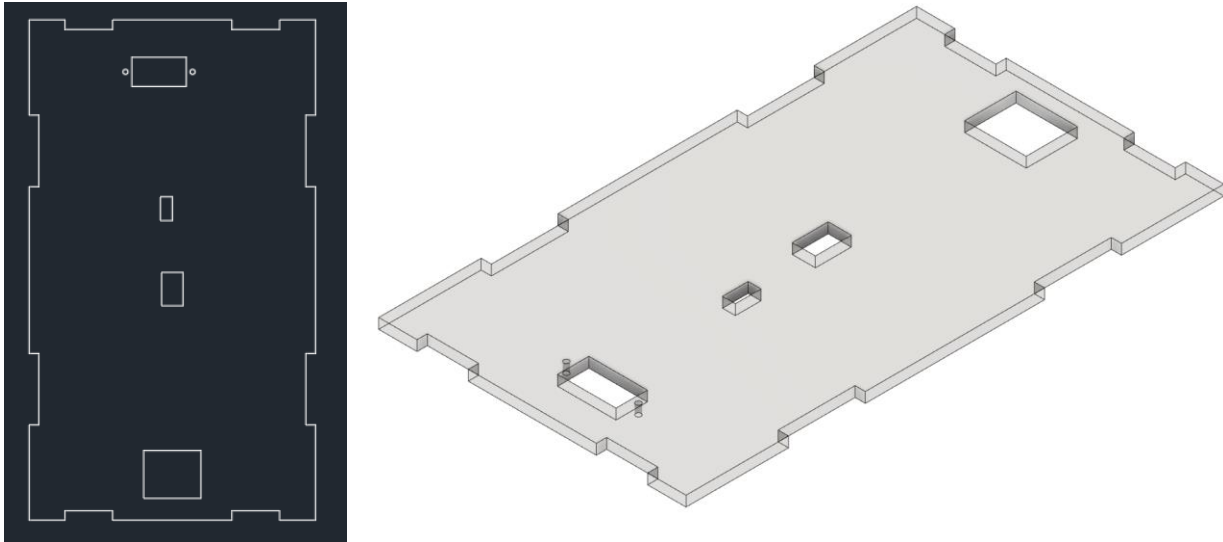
Diseño de la base de la estructura en el CAD Fusión 360 en vista isométrica
